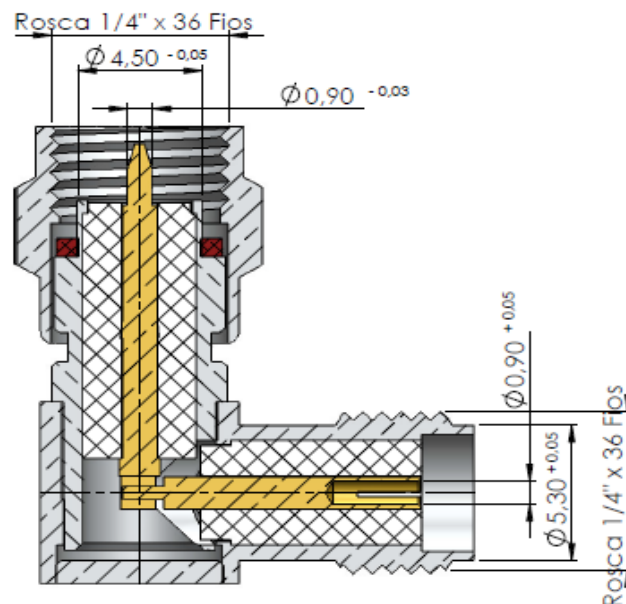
Dimensões de um Adaptador SMA Angular Macho e Fêmea
